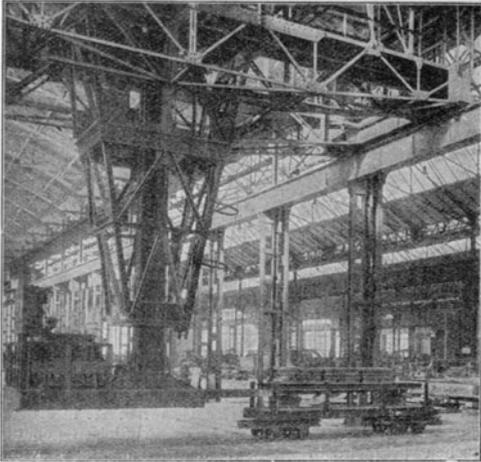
Entladung von Förderwagen mit zum Kran passender Platte durch Pratzekran.
